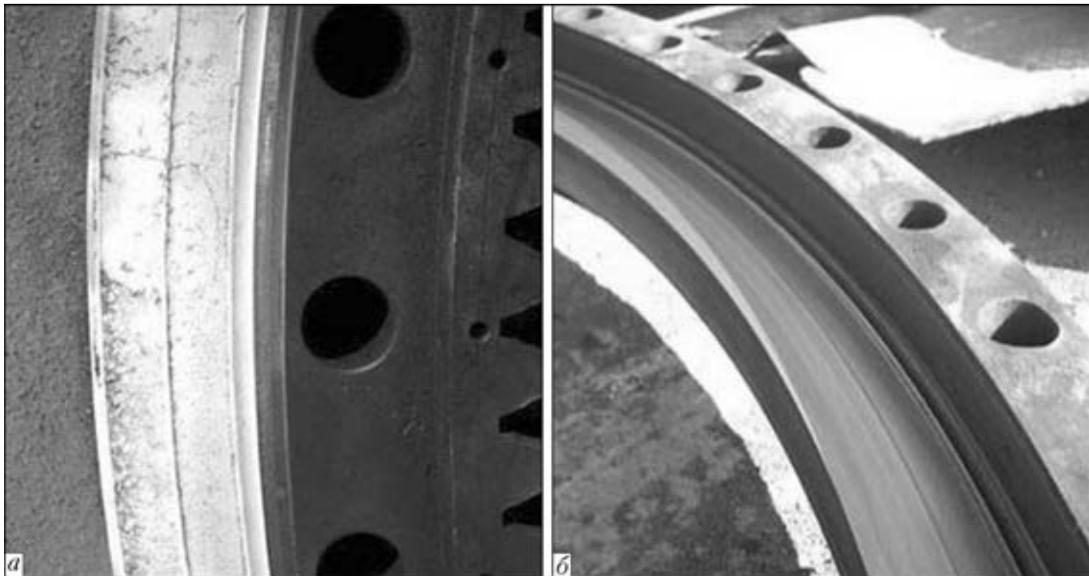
Внешний вид изношенных поверхностей катания зубчатого (а) и соединительного (б) колец ОПУ
